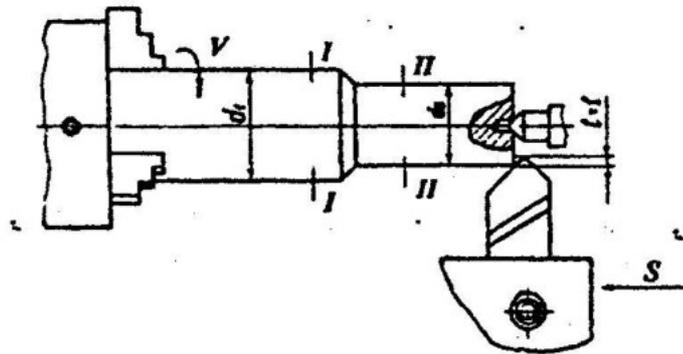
Установка ступенчатого валика в патроне и центре
